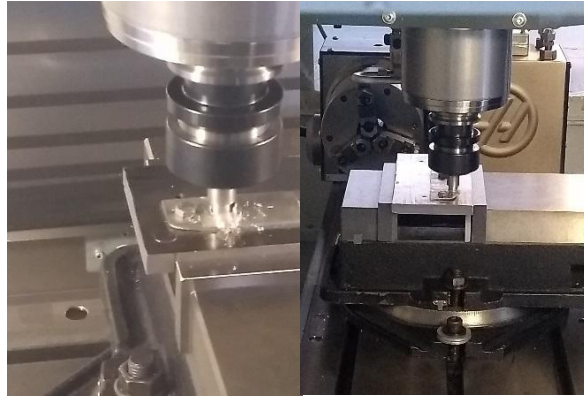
4 Aplicación de la soldadura FSW.
